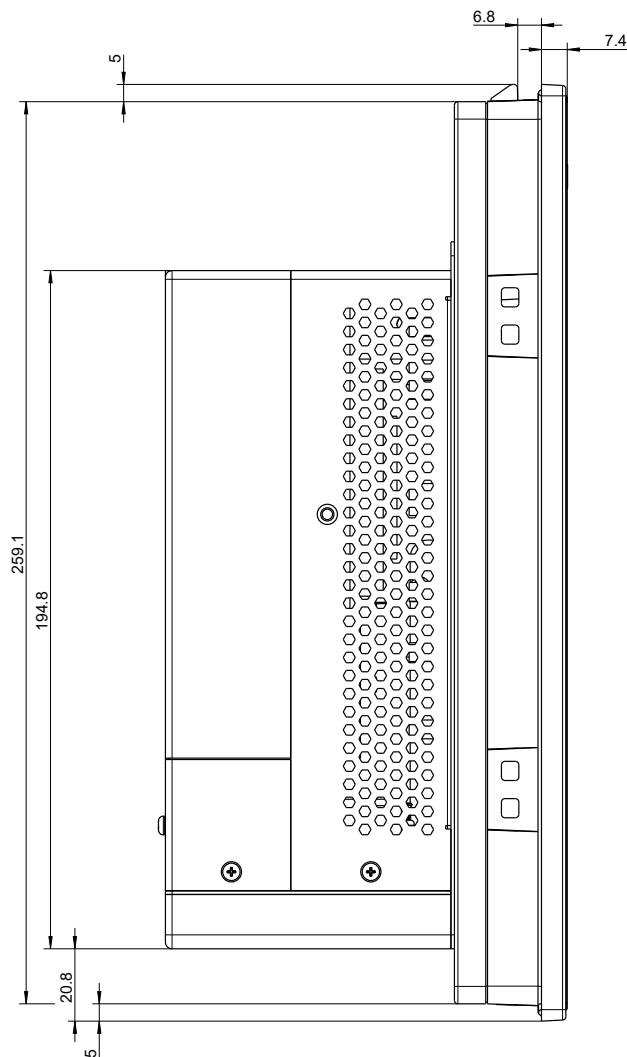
Размеры корпуса устройства VR4x15, вид слева
